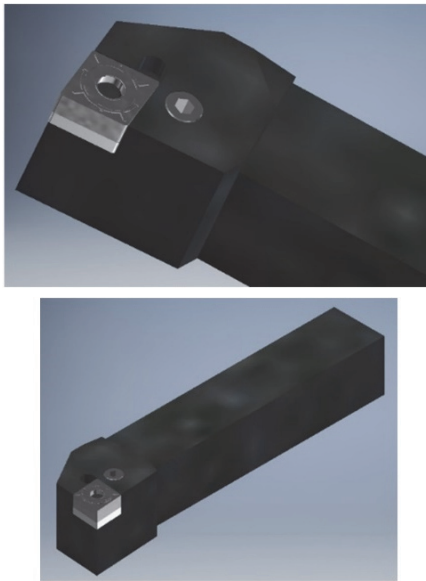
Резец для наружного точения PCLNR2525M12 (автор 3D-чертежа – К.Б. Дейнова)
